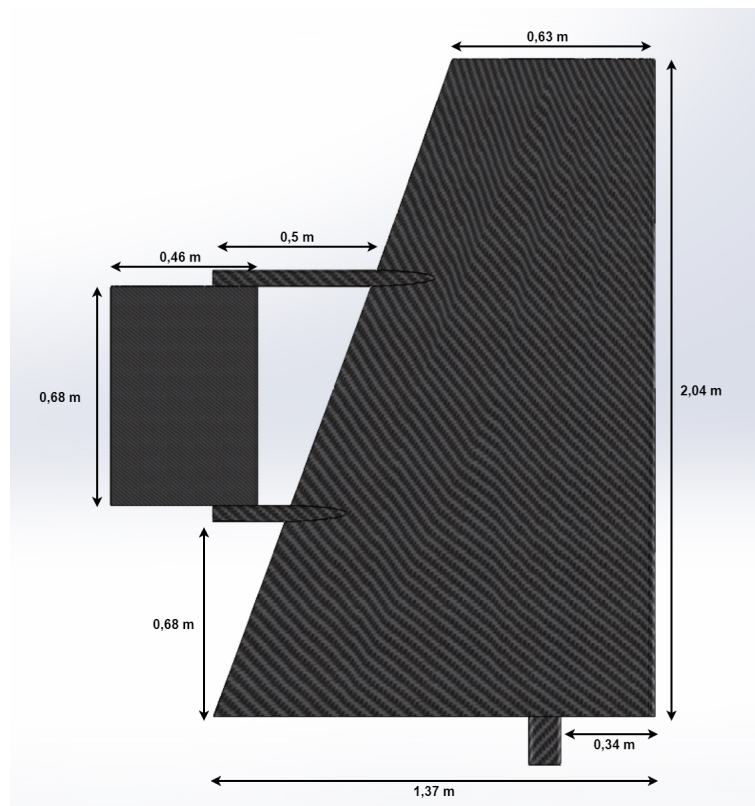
Dimensões do conjunto vela asa e cauda projetado
